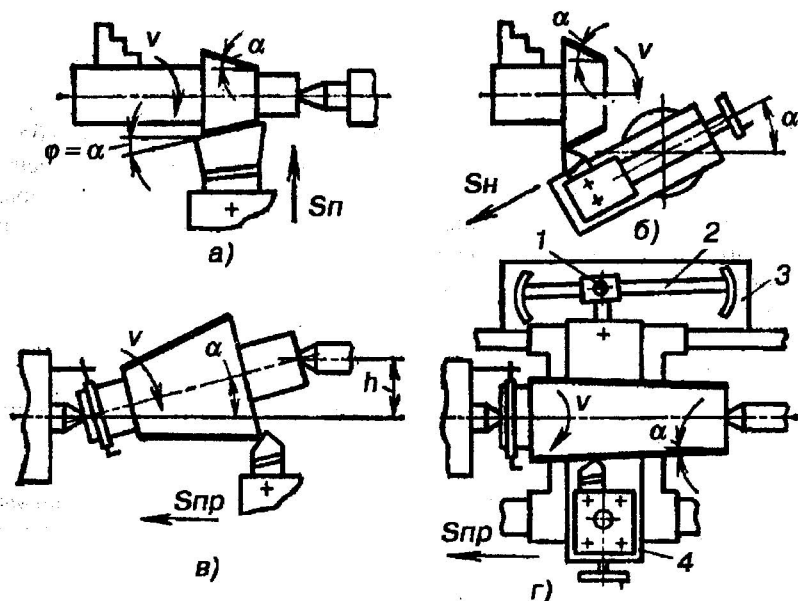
Схеми обточування зовнішніх кінцевих поверхнь на токарно-гвинторізному верстаті
